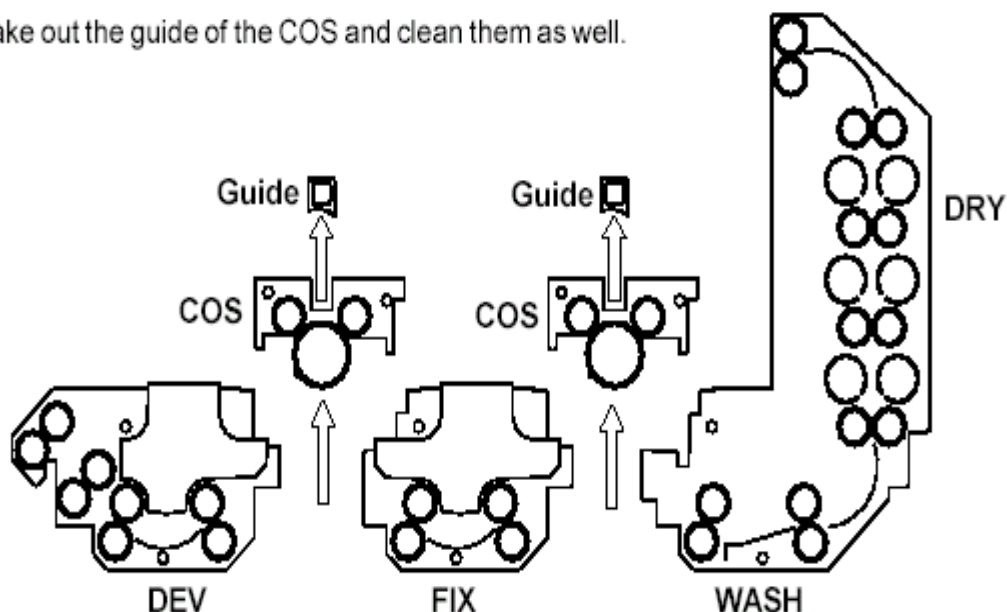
направляющая, 2- проявитель, 3- закрепитель, 4- промывка, 5- сушка, 6- разделитель
